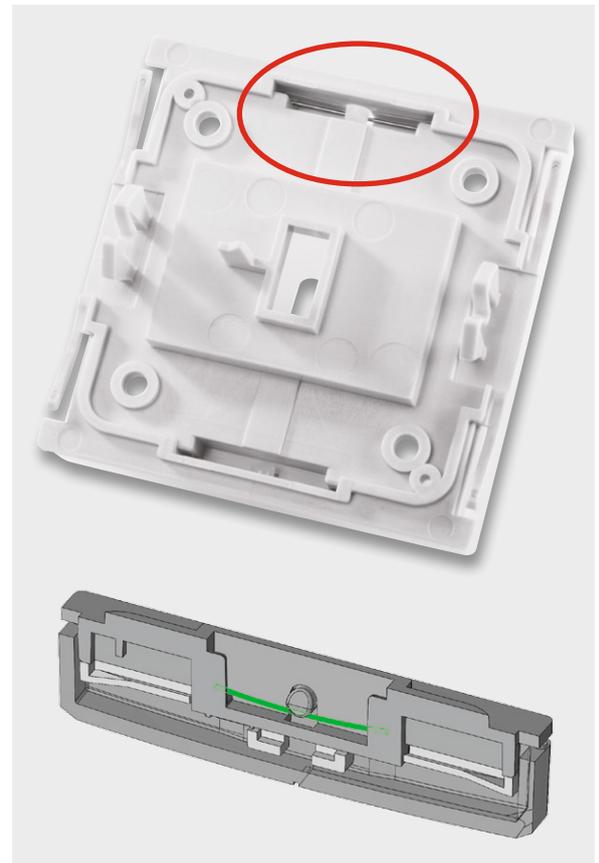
So sind die Federdrahtstücke in die Unterseite des Gehäuseteils einzusetzen.
